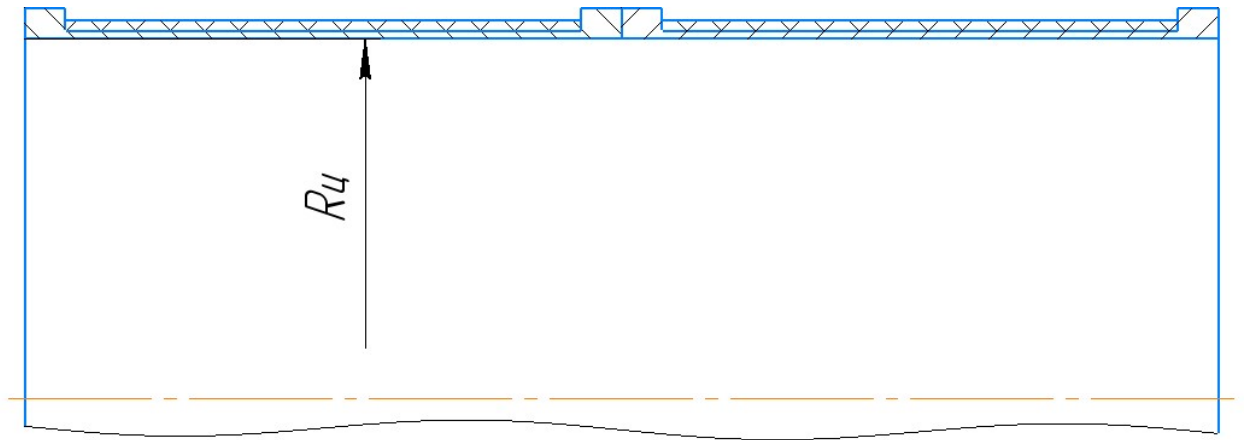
Концепция изготовления металлокомпозитной оболочки из сборных сегментов, эскиз
